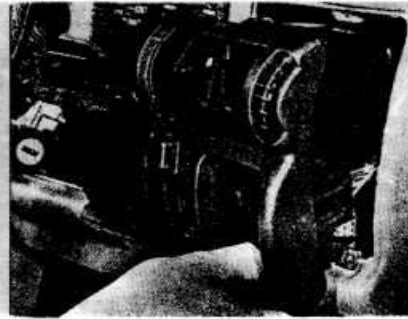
Извлечение корпуса вентиляционного сопла из панели
